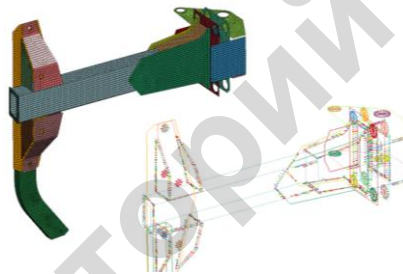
Упрощенная модель грядиля и стойки корпуса плуга
